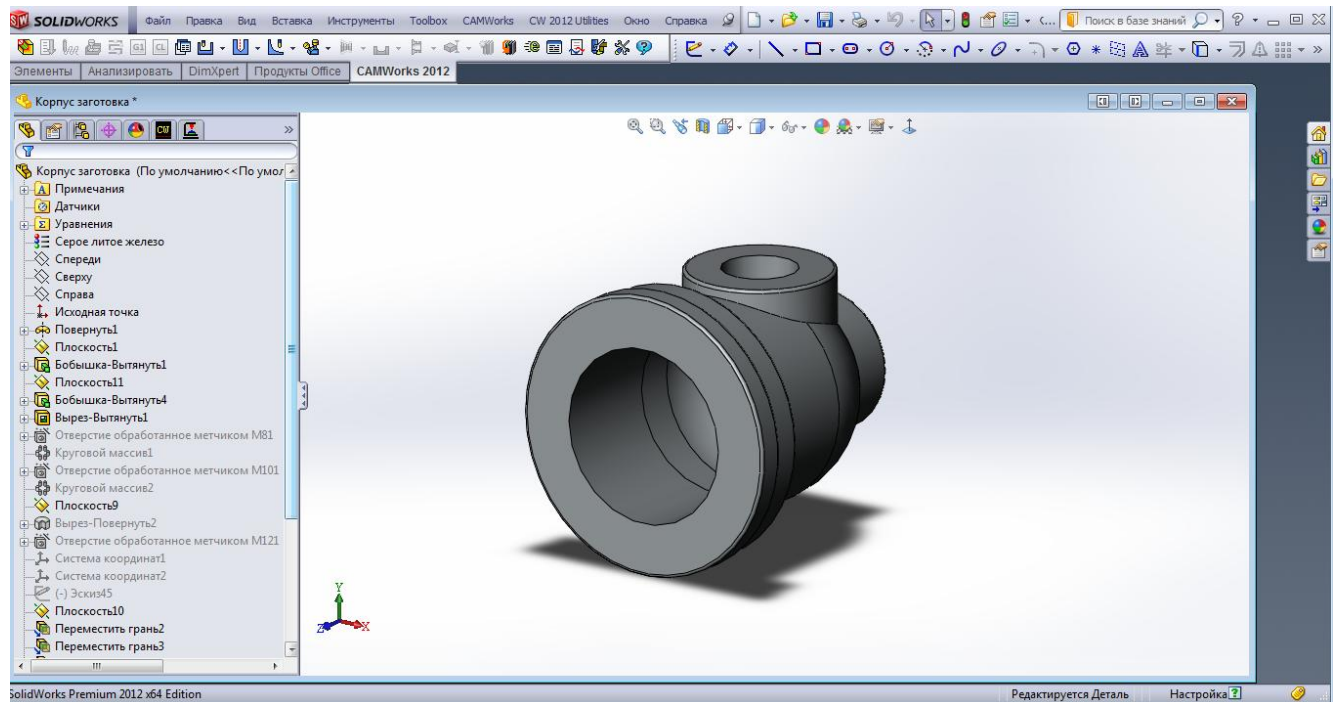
Модель заготовки «Корпус ДГК 10.030.20» з деревом побудови
